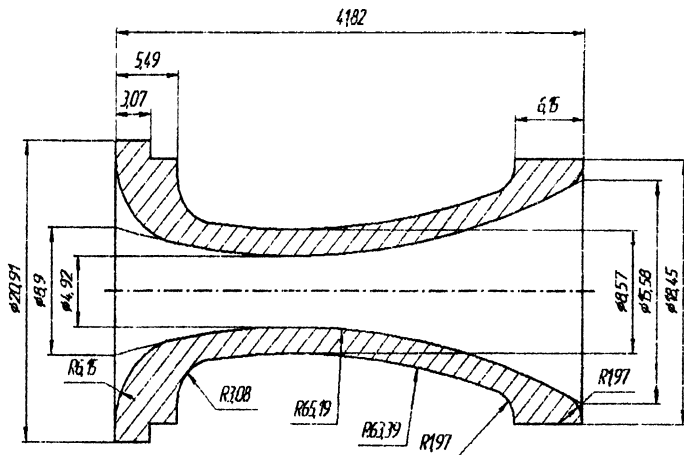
Эскиз прессовки детали «Проводка таза машин RI-10, RIR-15»
